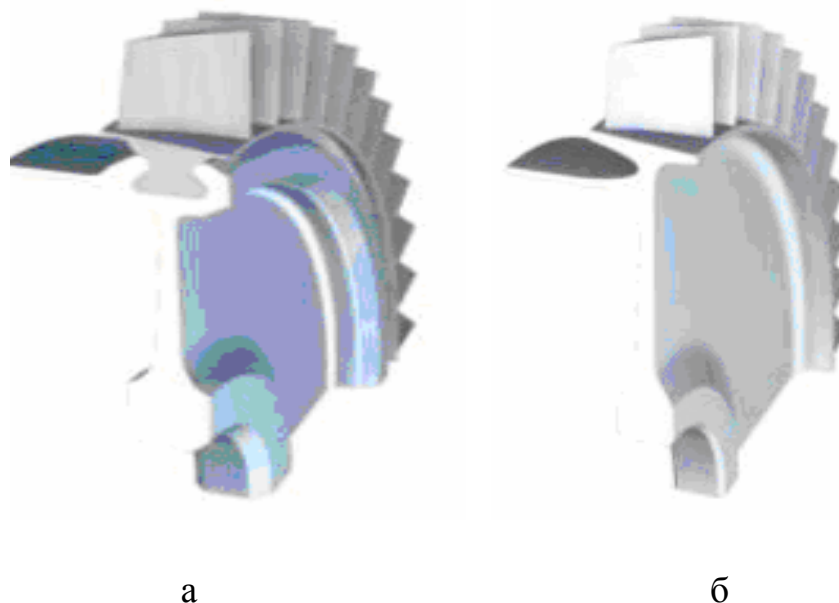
Внешний вид моноколеса и диска с лопатками:
